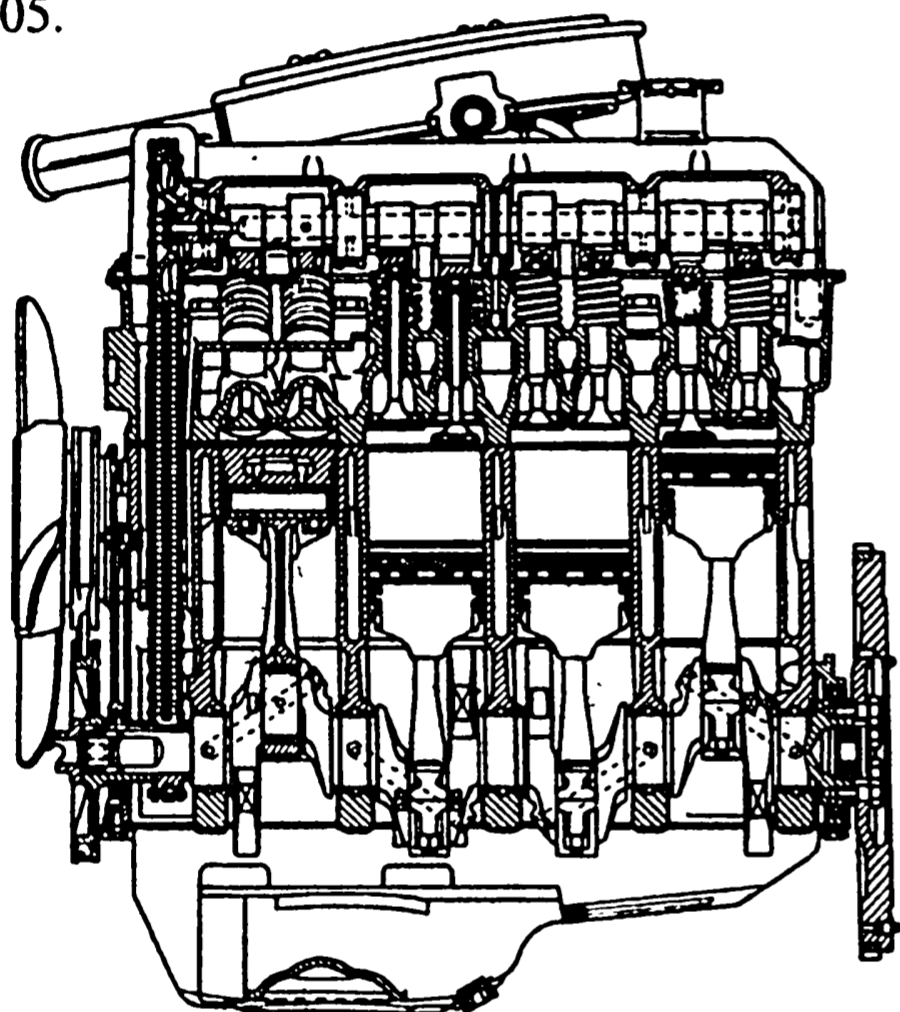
Продольный разрез двигателя ВАЗ-2101
